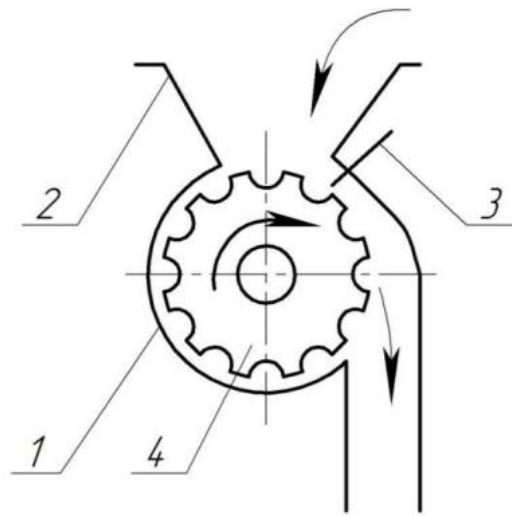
Барабанний дозувальний пристрій: 1 – корпус; 2 – накопичувач; 3 – засувки; 4 – котушка
